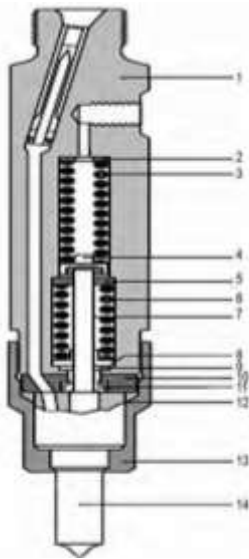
Паливна форсунка з двома пружинами [40]: 1 – корпус форсунки; 2 – прокладка; 3 – верхня пружина; 4 – натискний штифт; 5 – напрямний елемент; 6 – нижня пружина; 7 – штанга; 8 – прокладка пружини; 9 – прокладка; 10 – проміжний елемент; 11 – стопорна втулка; 12 – голка розпилювача; 13 – накидна гайка; 14 – розпилювач форсунки
